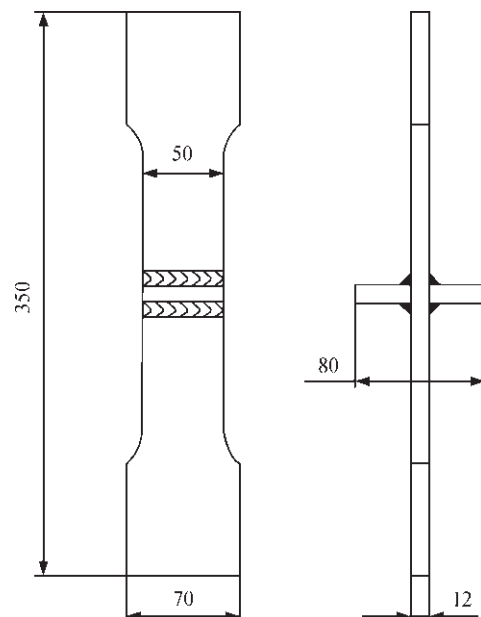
Форма и геометрические размеры образцов таврового сварного соединения
